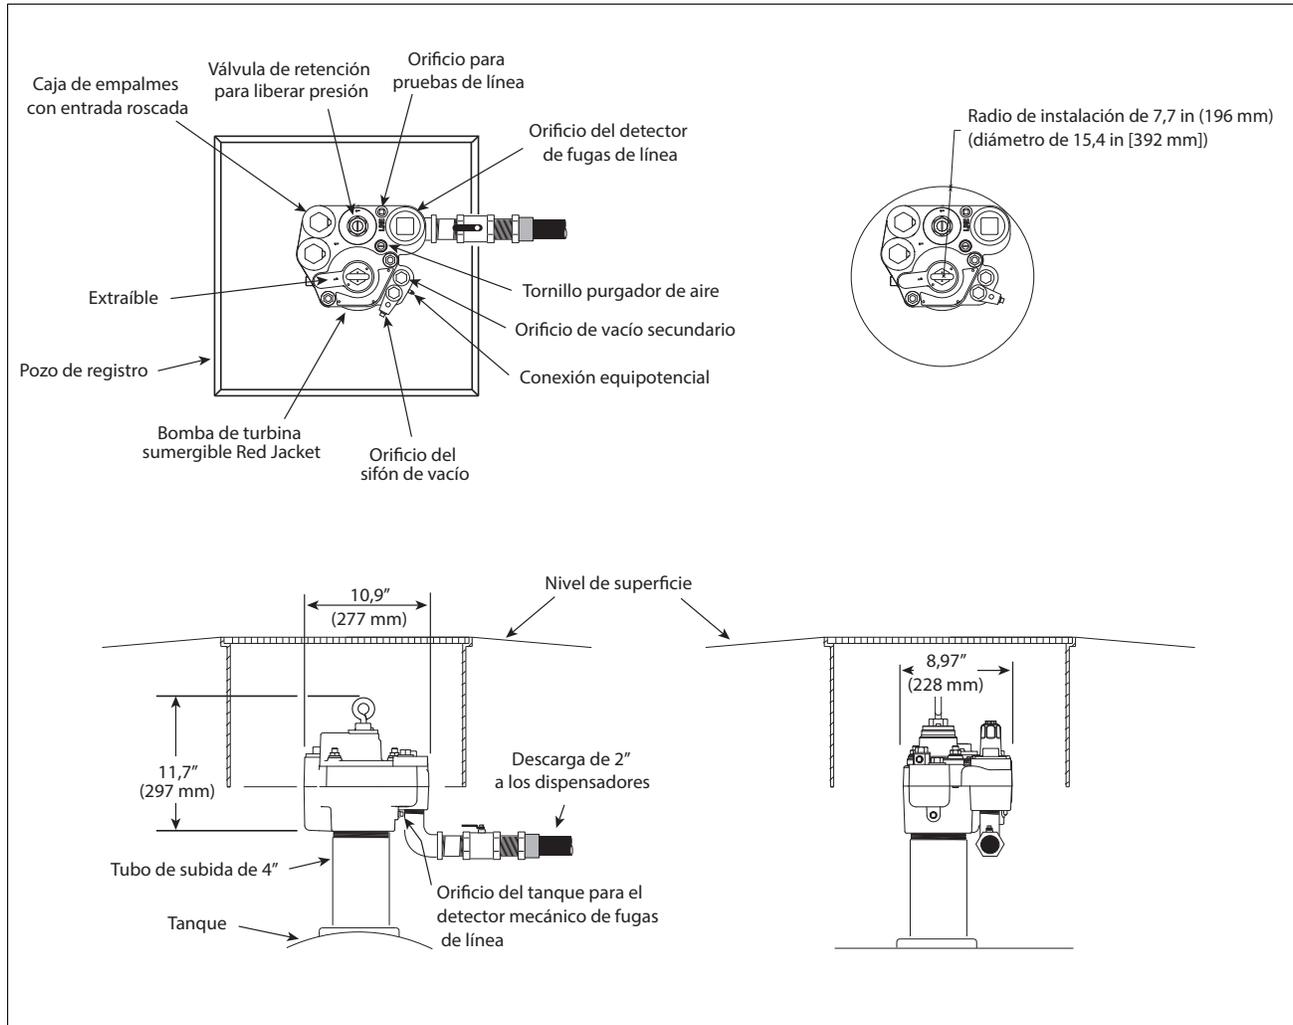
Componentes y dimensiones del empaquetador-distribuidor Red Jacket
